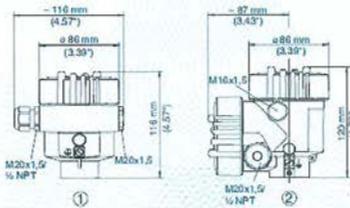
Алюмінієвий корпус (1 – однокамерний; 2 - двокамерний)
